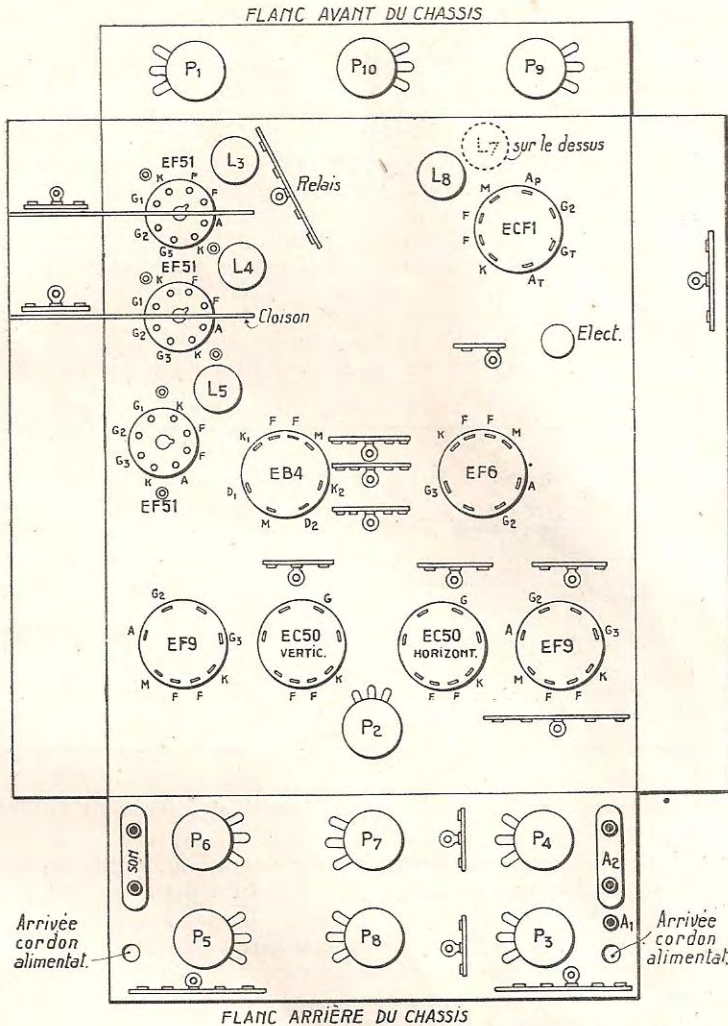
Disposition des éléments constitutifs et des blindages du châssis du récepteur vu par dessous.
